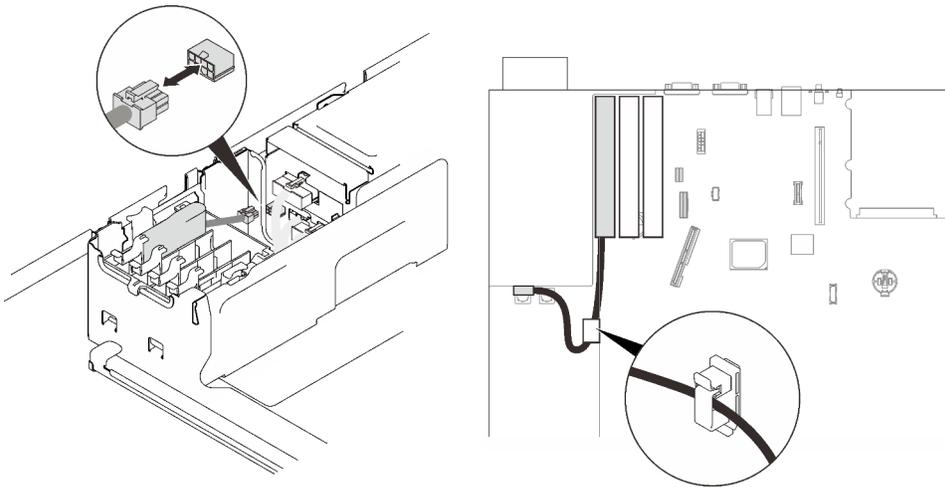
Collegamento dei cavi del modulo di alimentazione flash
